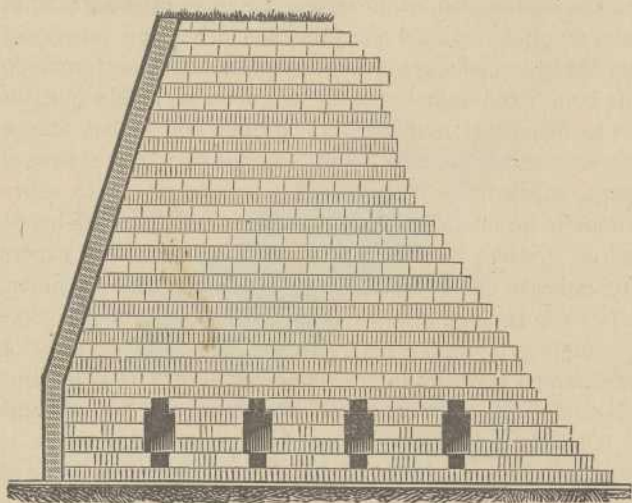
Hormiguero para cocer ladrillos en una tejería rural; alzado.
